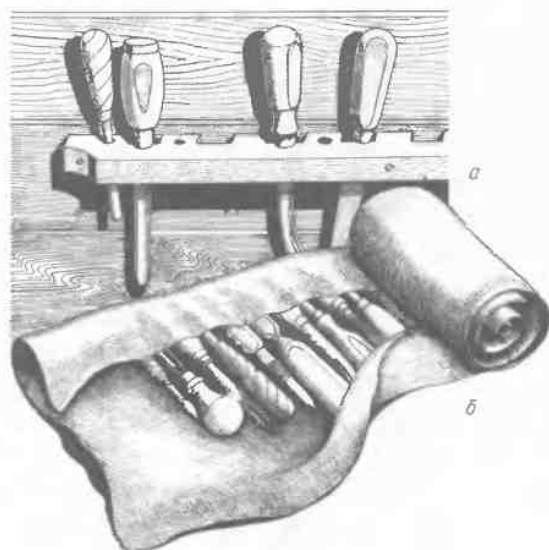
Хранение стамесок: а — на рабочем месте; б — при перевозке или длительном хранении
